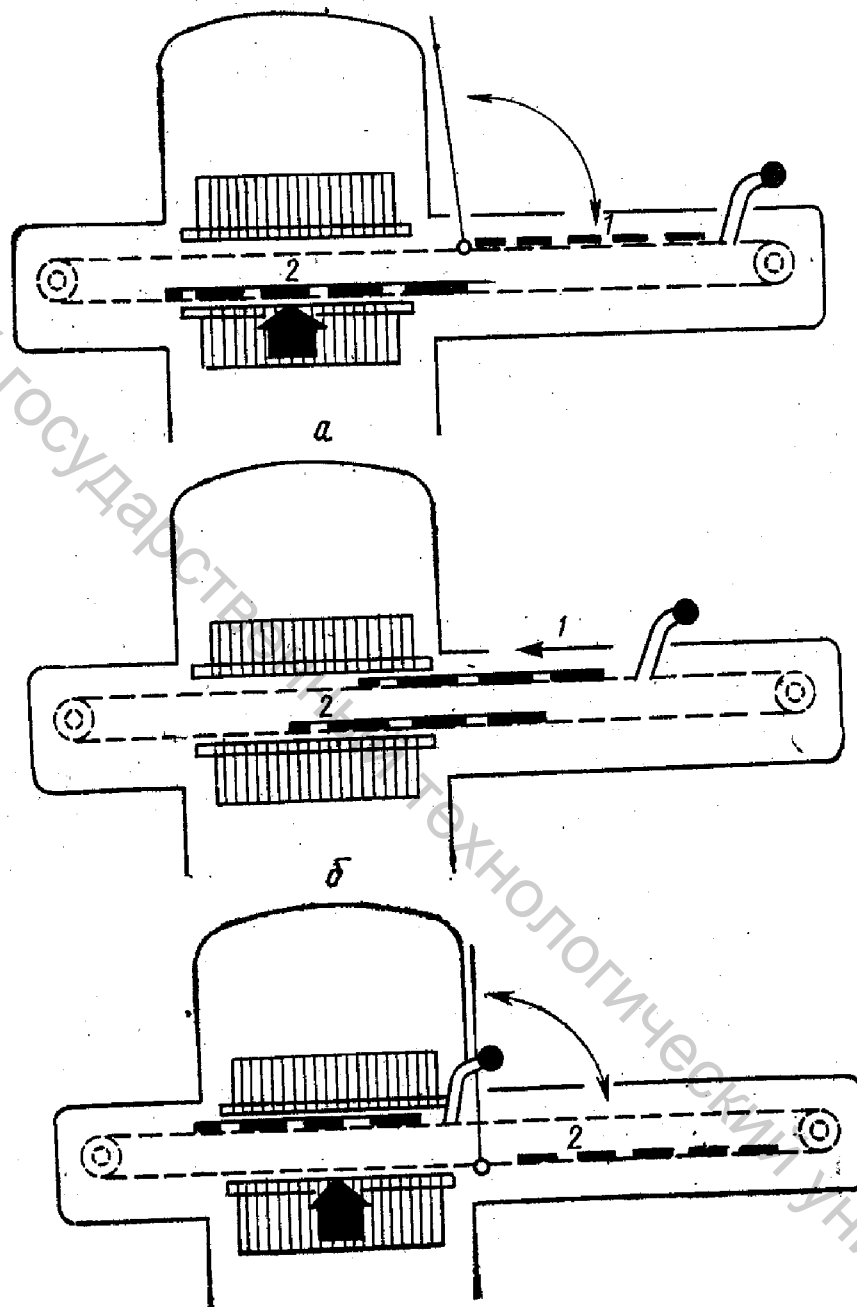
Малогабаритный пресс для дублирования мелких деталей
